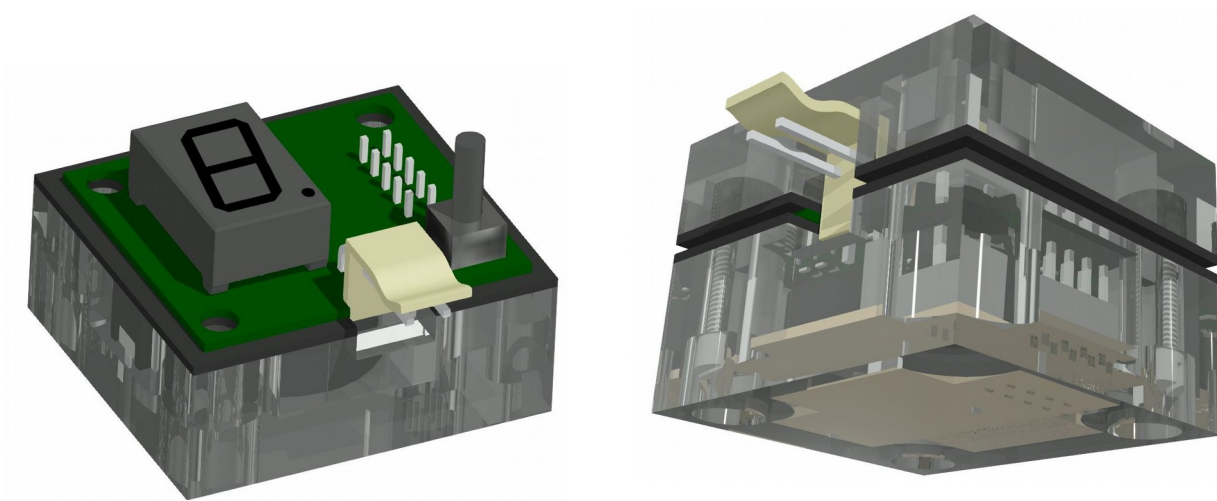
Внешний вид платы измерителя в сборе.
